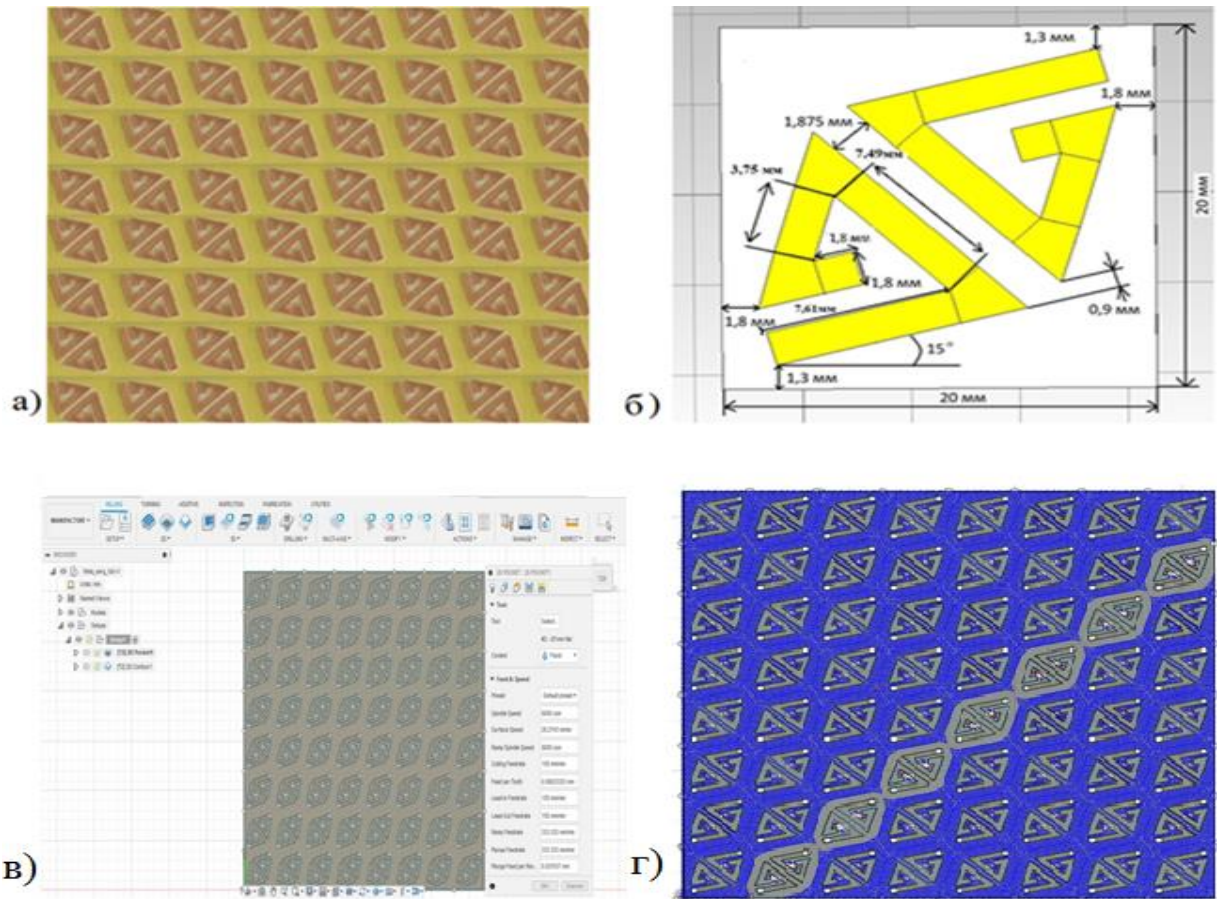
Экспериментальный образец треугольной метаповерхности: (а), геометрические параметры единичных разомкнутых треугольных резонаторов (б), маршрут движения фрезеровки (в), модель метаповерхности в специализированной прикладной сборке Fusion версии 360 (г)
